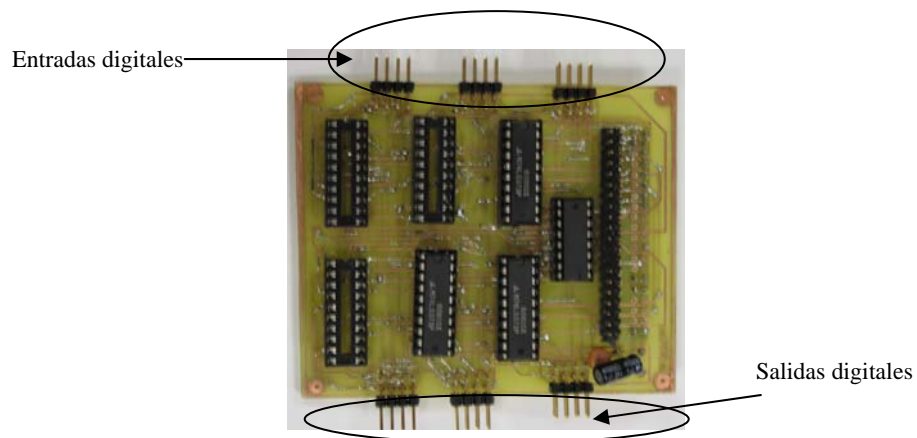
Ensamble físico de la tercera parte de la tarjeta de control.
